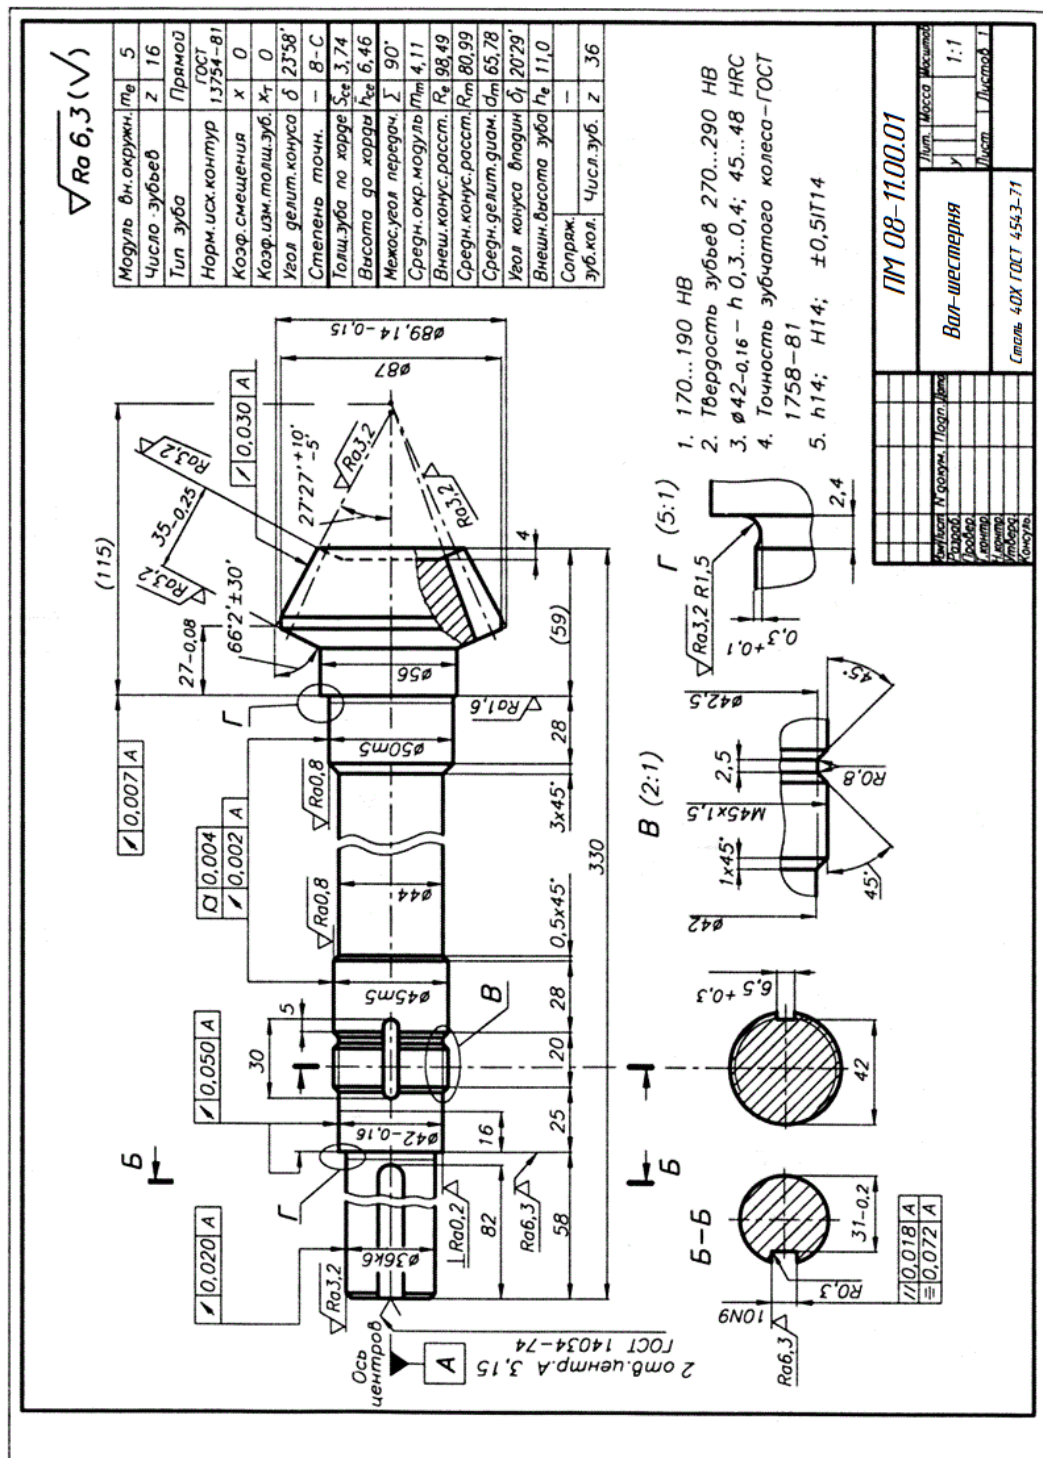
Пример рабочего чертежа вал-шестерни конической
